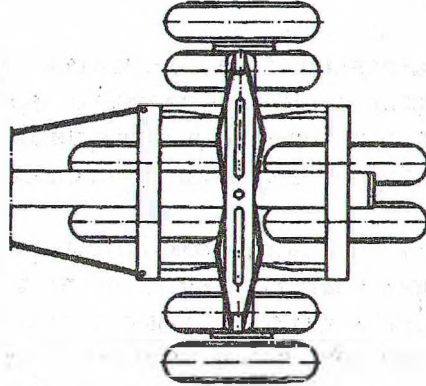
Конструкция прицепа-ропуска (вид сверху)
